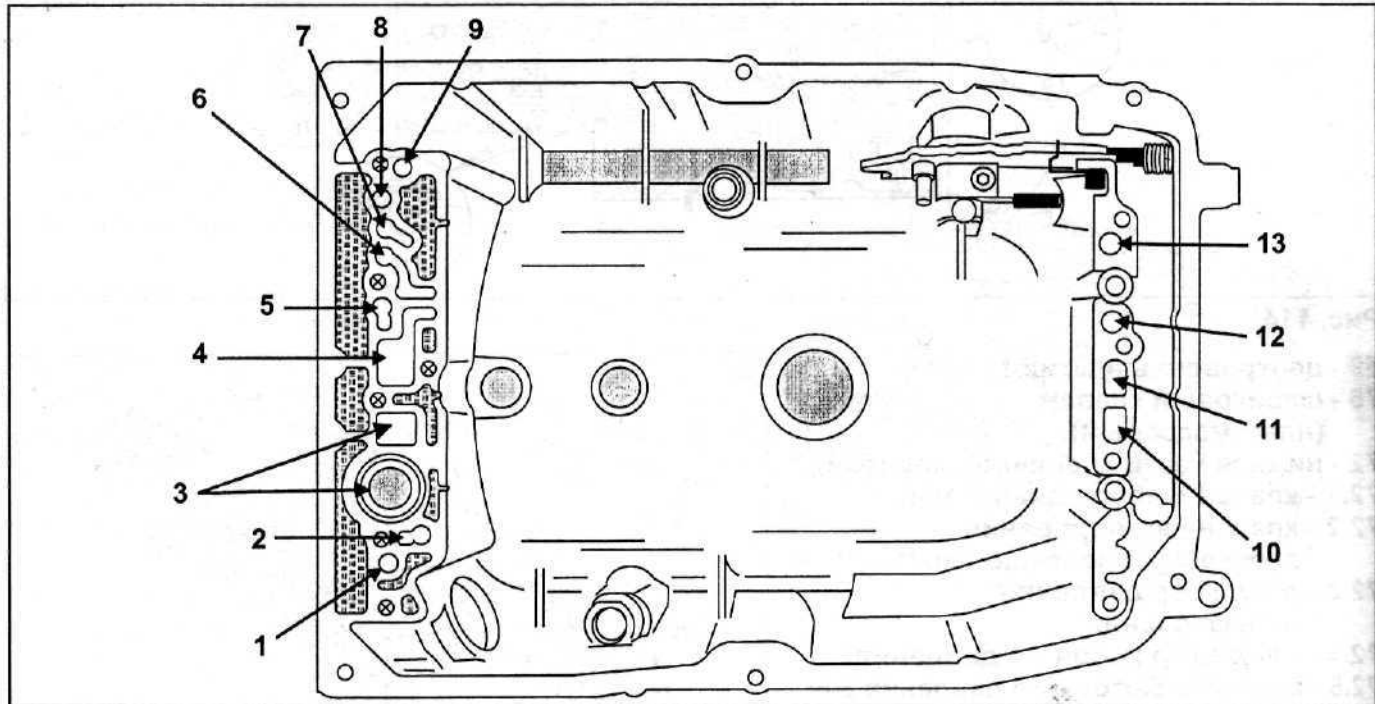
Назначение отверстий в картере коробки передач (со стороны клапанной коробки).
